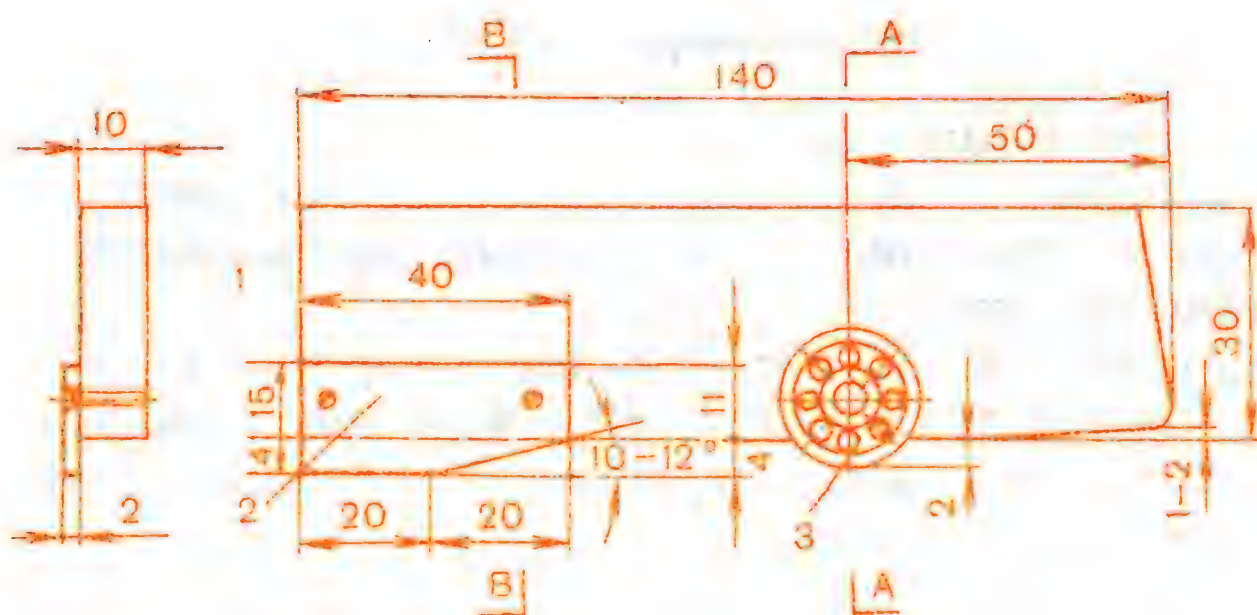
Каретка фоторезака: 1 — корпус, 2 — направляющие стальной планки, 3 — подшипник
